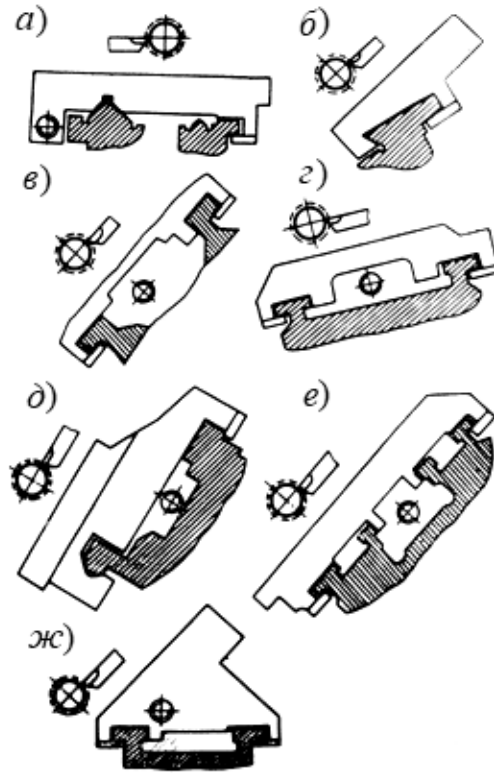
Направляющие скольжения суппортов односуппортных токарных станков
